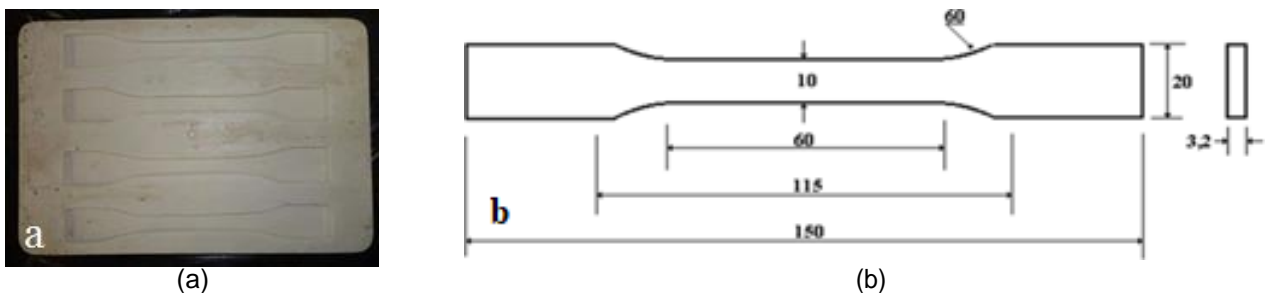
(a) Molde de silicone e (b) as dimensões da norma ASTM D 638M.
